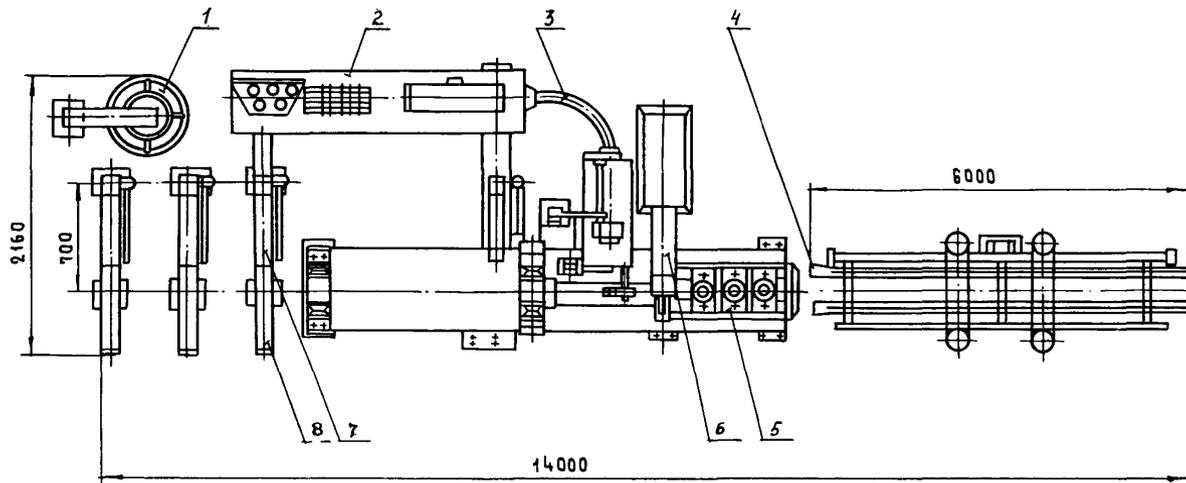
Рис. II. Полуавтоматическая линия для сварки двухветвевых каркасов:
